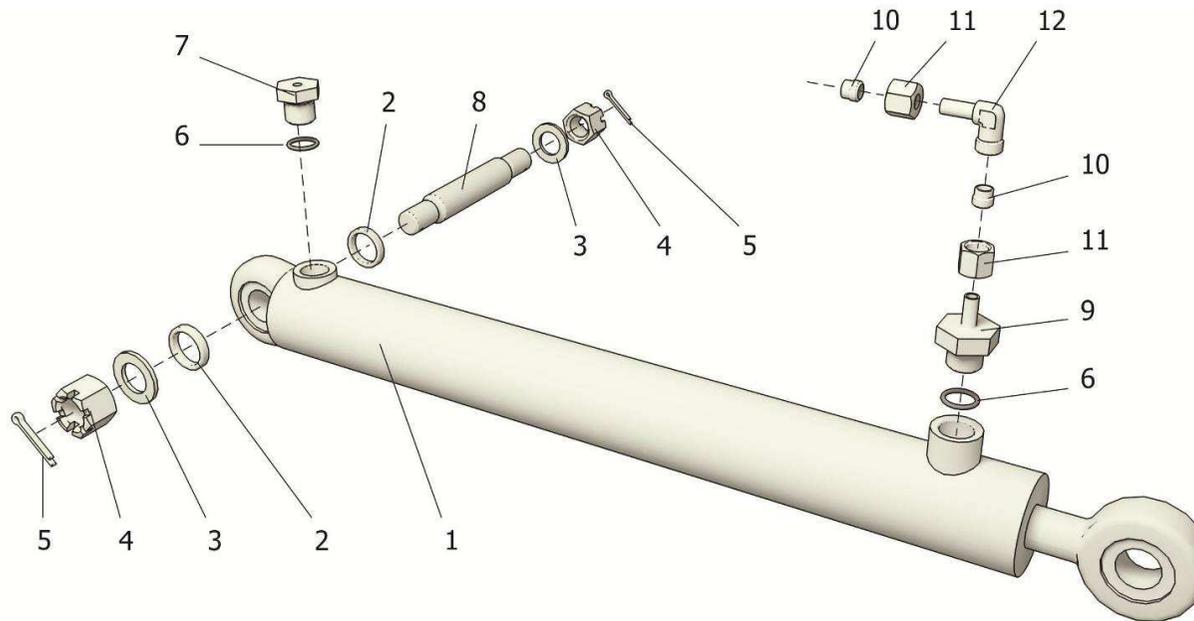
Гидроцилиндр КРП-302.09.080Б-01
